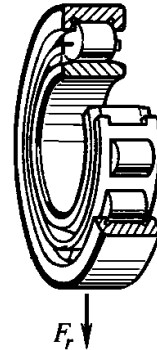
Роликовый радиальный подшипник с короткими цилиндрическими роликами
